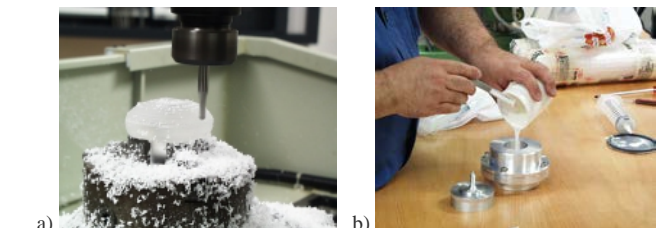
Processo de fabrico das lentes. a) Por CNC; b) Por moldagem.
